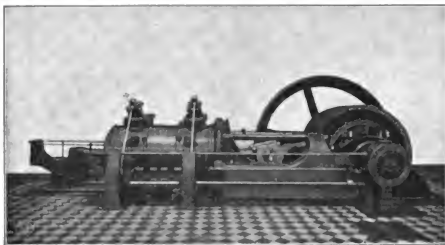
Gasmaschine der Maschinenbau-Akt.-Ges. Union
